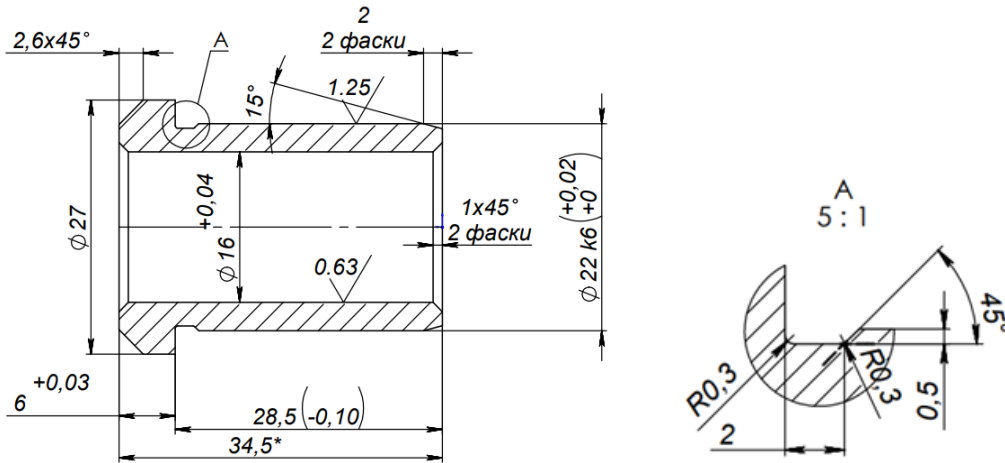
Приклад деталі, що виготовляється за одну операцію
